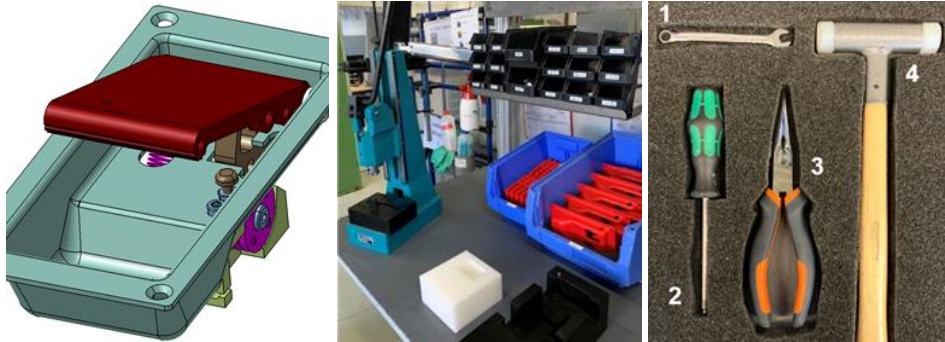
3-D-Modell des zu montierenden Notgriffs (links); Montagearbeitsplatz mit Teilelagern, Montagevorrichtungen und eine Einpressvorrichtung (mittig); für die Montage benötigtes Werkzeug (rechts): Ring-Maulschlüssel SW 8 (1), Innensechskantschlüssel SW 4 (2), Spitzzange (3), Kunststoffhammer (4)
